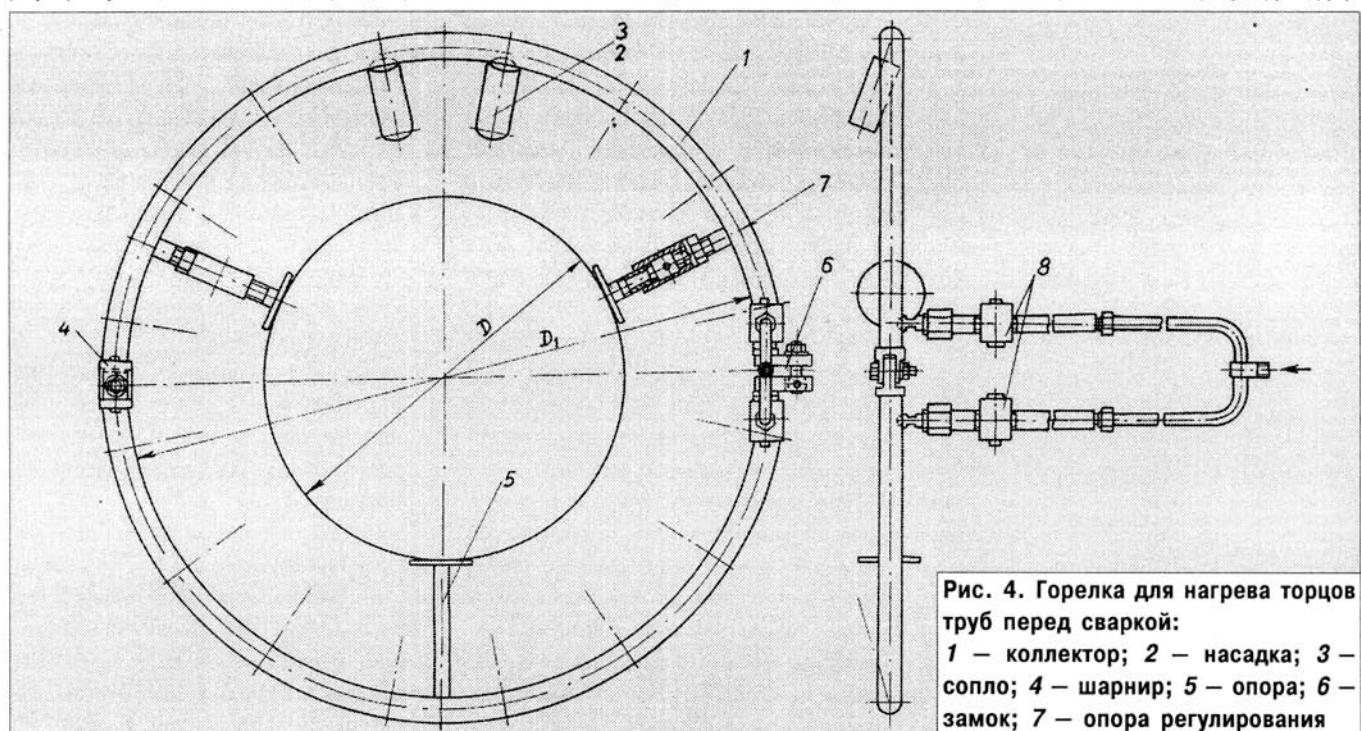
Горелка для нагрева торцов труб перед сваркой:
